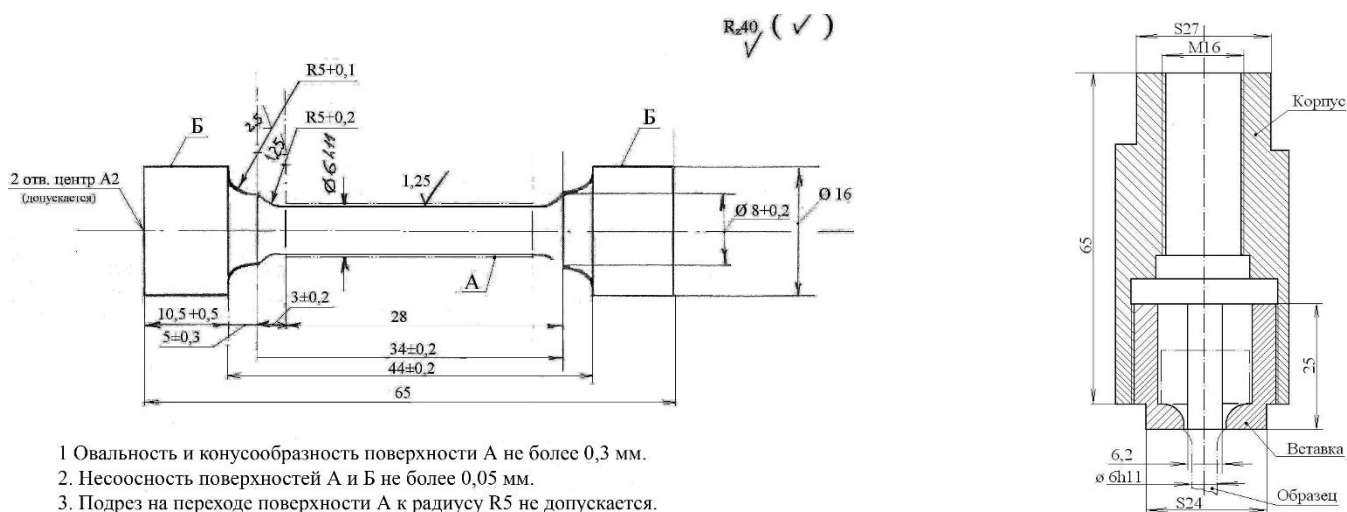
Образец и захваты для крепления образца в испытательной машине
